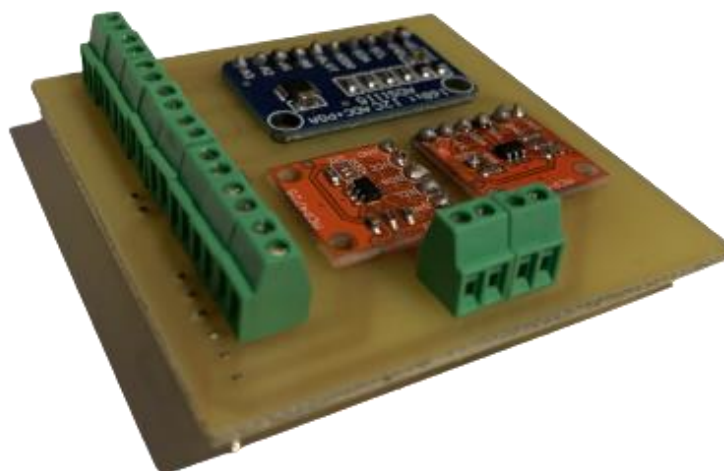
PCB COMPLETA CON DISPOSITIVOS Y TERMINALES SOLDADOS
